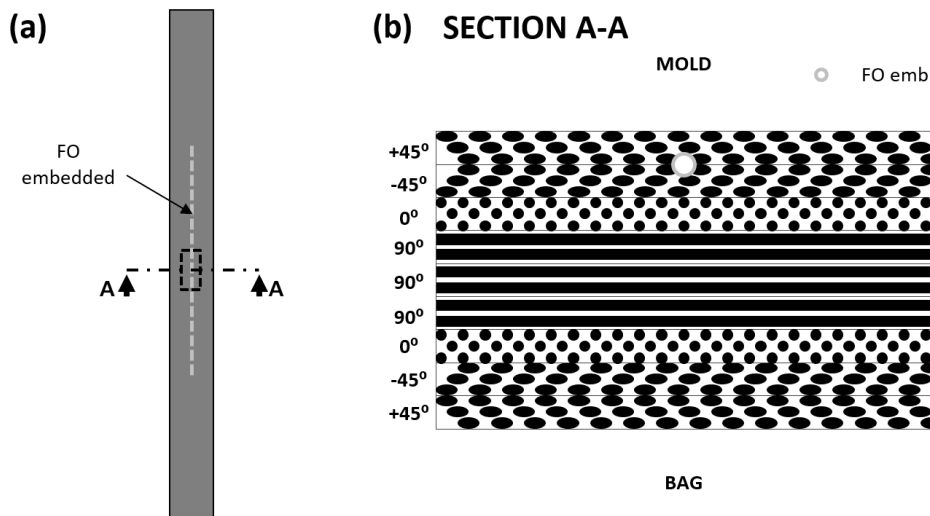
Probetas ensayo fatiga instrumentada con fibra óptica embebida (a) esquema en planta y (b) corte transversal.
